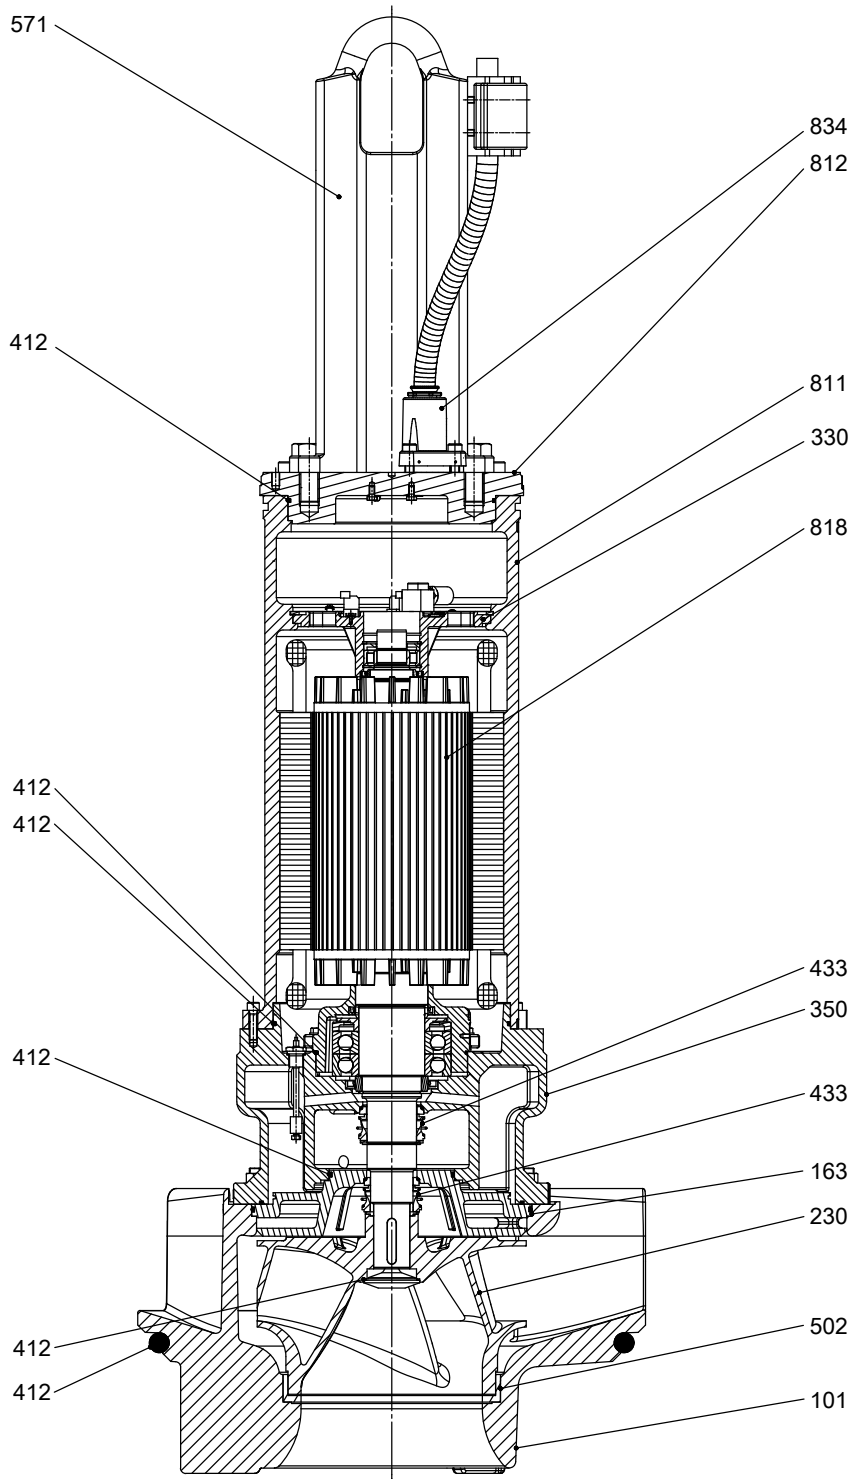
Gesamtzeichnung, Motorversion UN, XN
